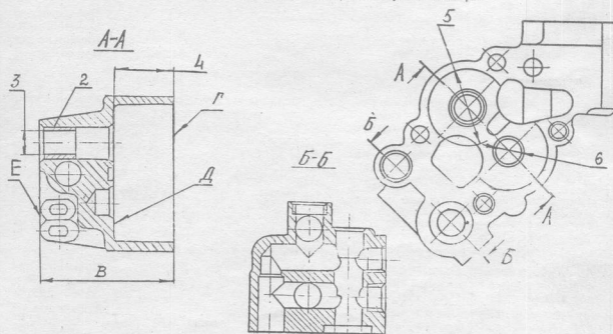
Корпус нагнетающей секции со втулкой в сборе
